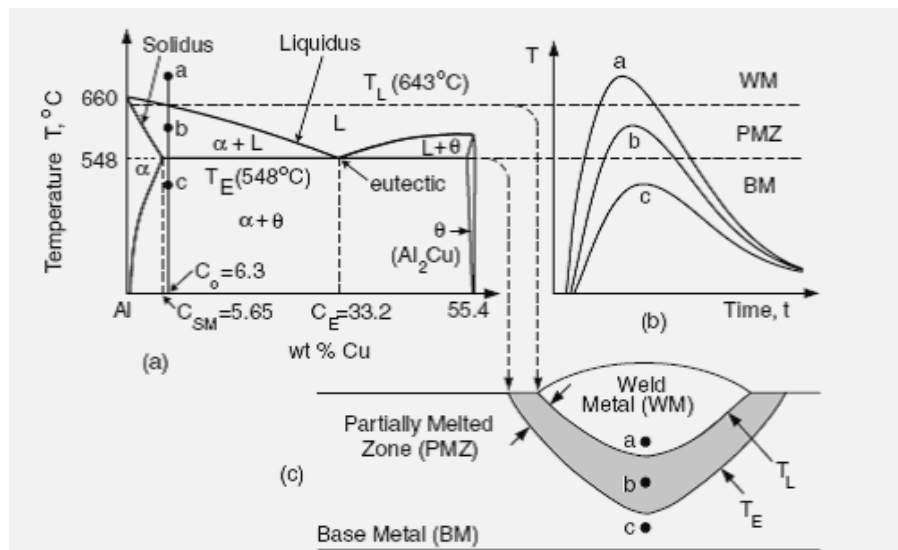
(12.3) Formation de ZL dans la soudure d'aluminium 2219: (a) diagramme de phase Al-Cu; (b) cycle thermique; (c) cordant de soudure [17].
